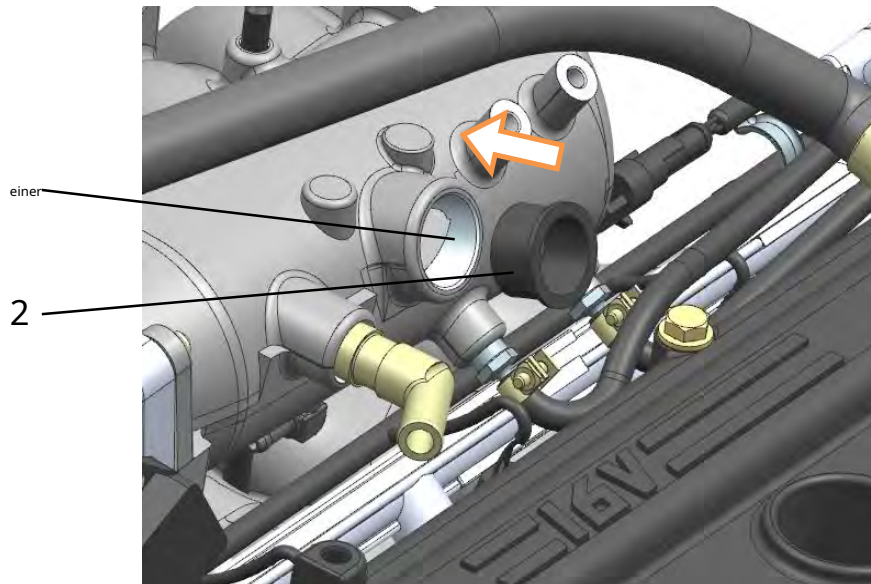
Einbau des O-Rings des Leerlaufreglerrohrs:
